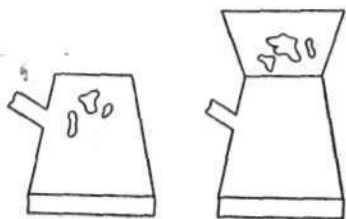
Слева — отливка с усадочными раковинами в ее верхней части.
